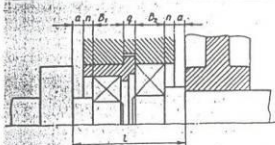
Компоновка подшипникового узла соосного редуктора
